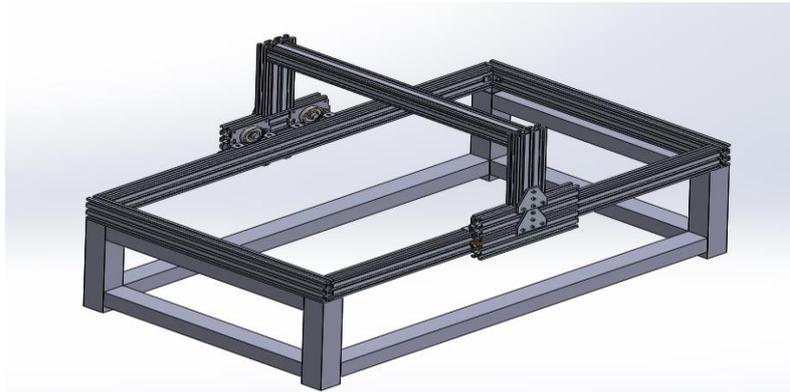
Assemblage de la structure du bâti de la machine CNC 5
